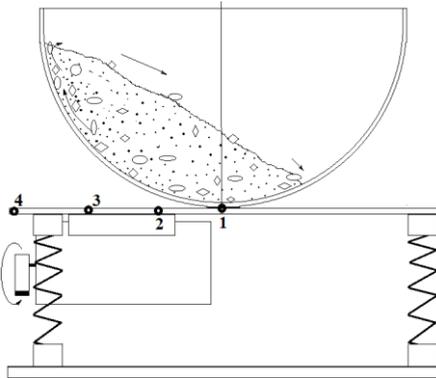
Схема установки для обработки незакрепленных деталей в свободном абразиве.
